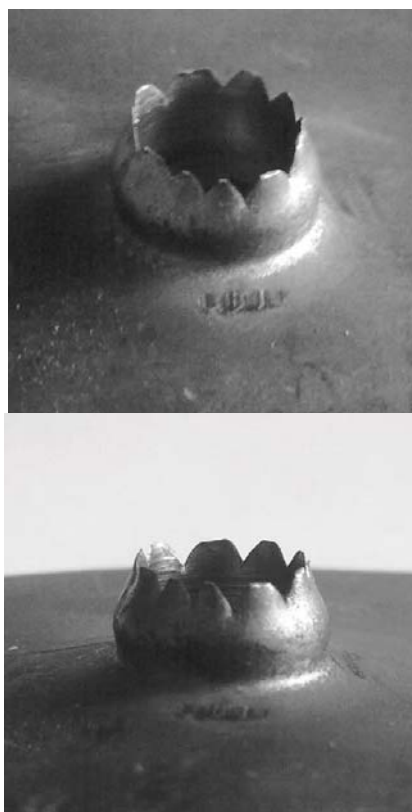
Нижняя часть узла крепления. Подача 160 мм/мин. Инструмент с конической формой рабочей части.
